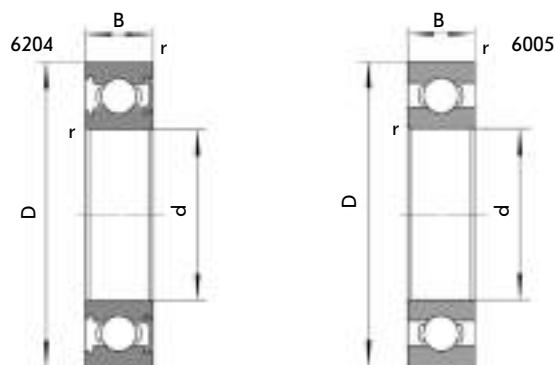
Основные размеры подшипников марок 6204 и 6005
